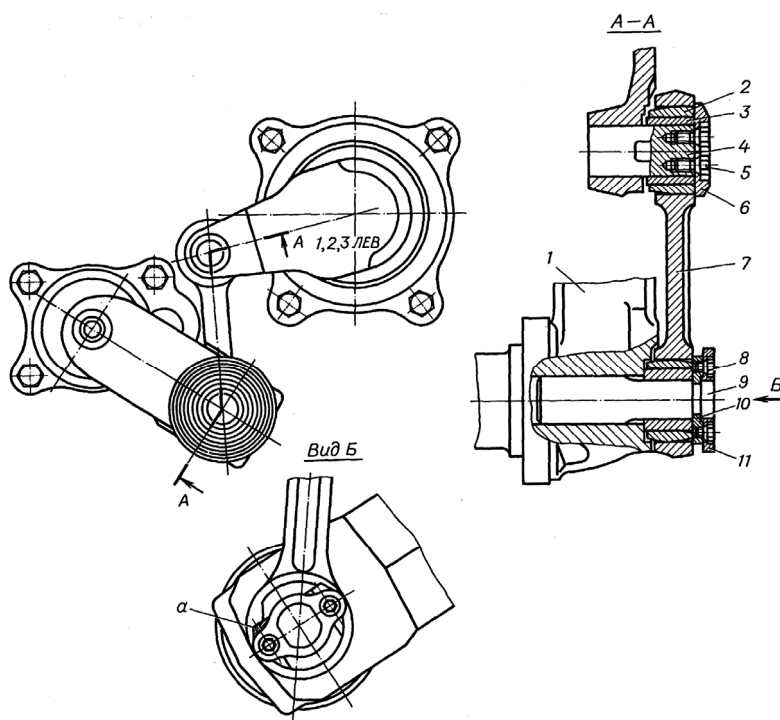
Шарниры гидроамортизатора: 7 – балансир; 2 – наружная втулка; 3 – внутренняя втулка; 4 – палец рычага гидроамортизатора; 5, 8 – болты; 6, 11 – крышки; 7 – тяга; 9 – палец балансира; 10 – шайба; а – отверстие
